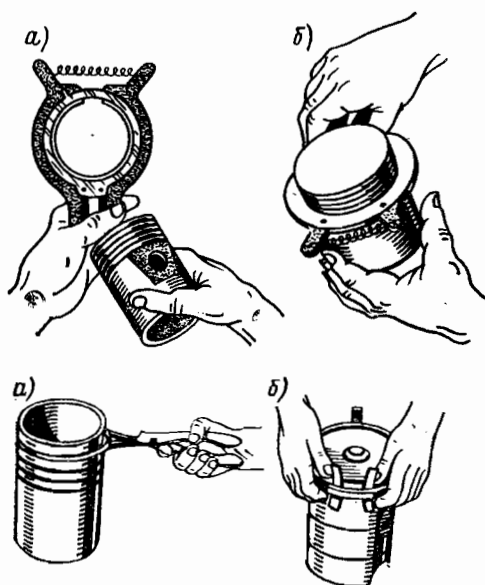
Приспособление для установки и снятия поршневых колец: *а* — положение перед установкой кольца; *б* — надевание кольца
